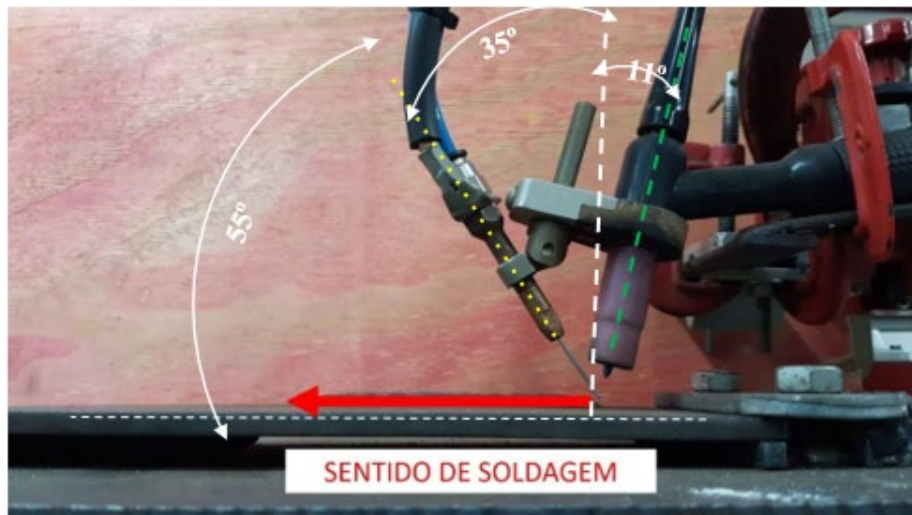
Tocha GTAW acoplada ao trator de soldagem.
